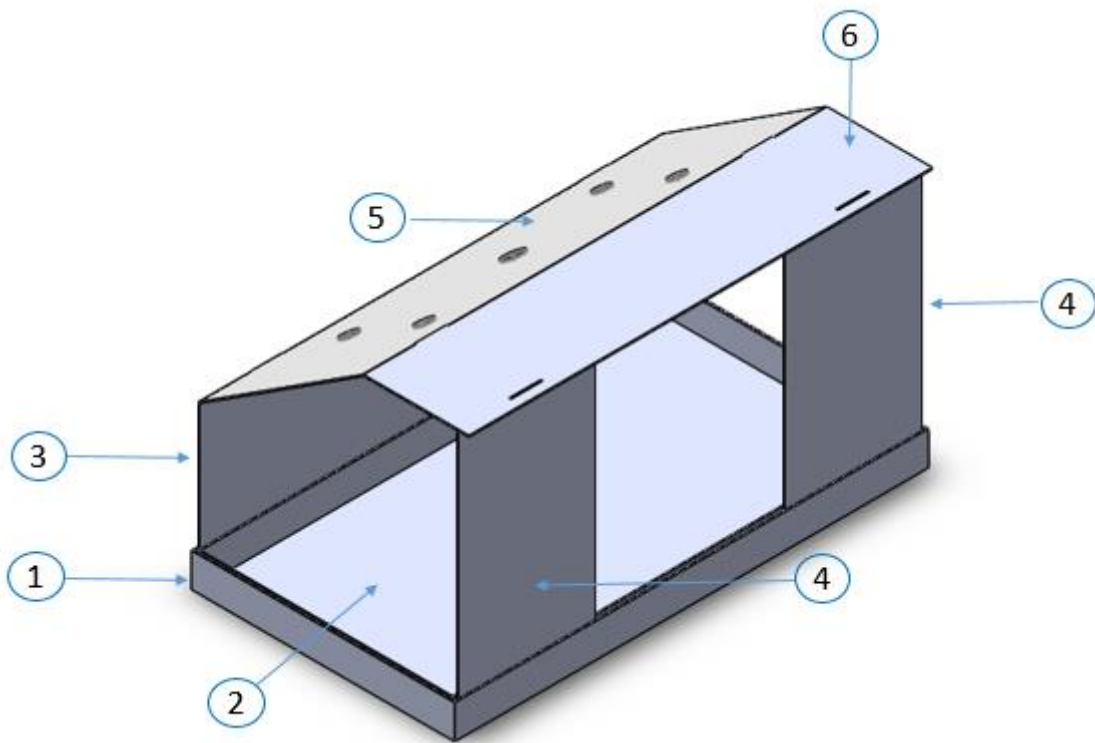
Vista em perspectiva da parte posterior da Caixa e seus componentes [Tampa (1); Base (2); Suporte Frontal (3), Suportes Traseiros (4), Superfície Inclinada (5) e Superfície Superior (6)].
